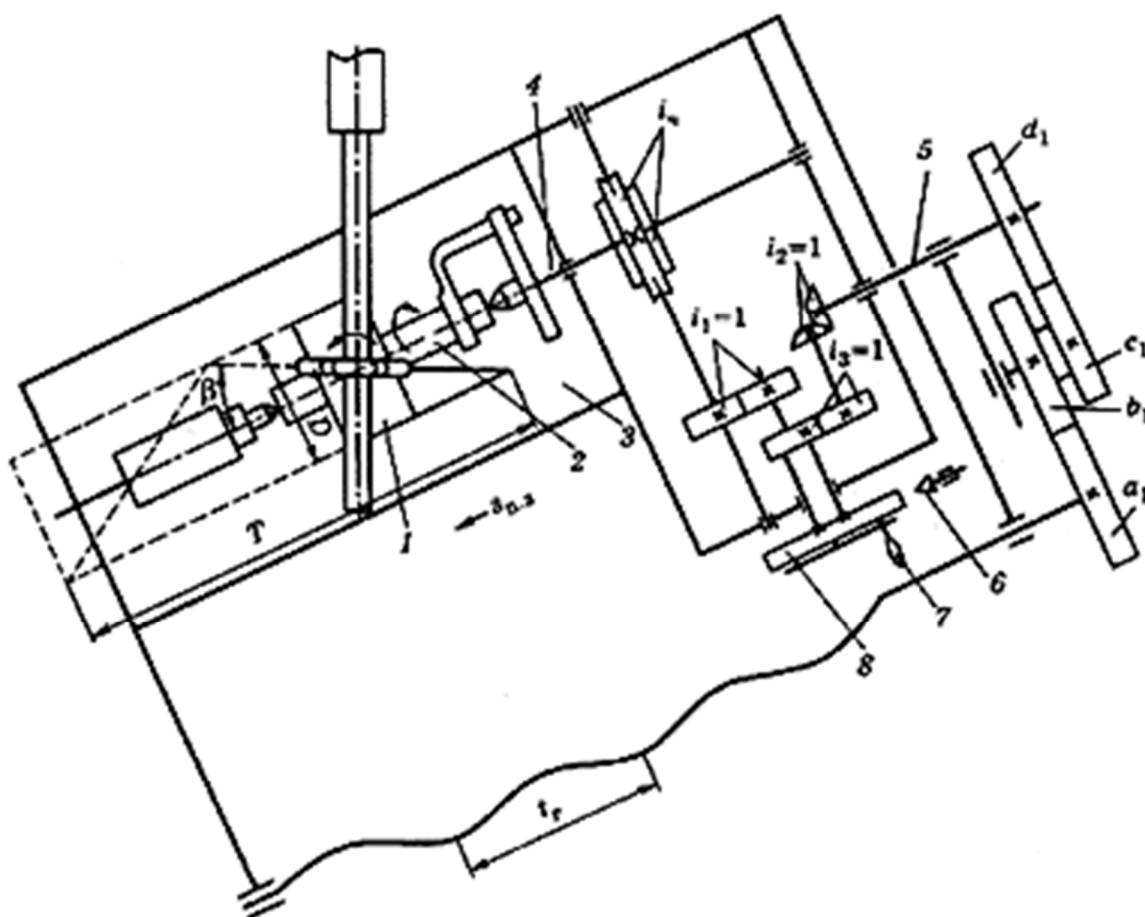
Схема настроювання універсально-фрезерного верстата і ділильної головки на фрезерування гвинтових канавок (косих зубів)
